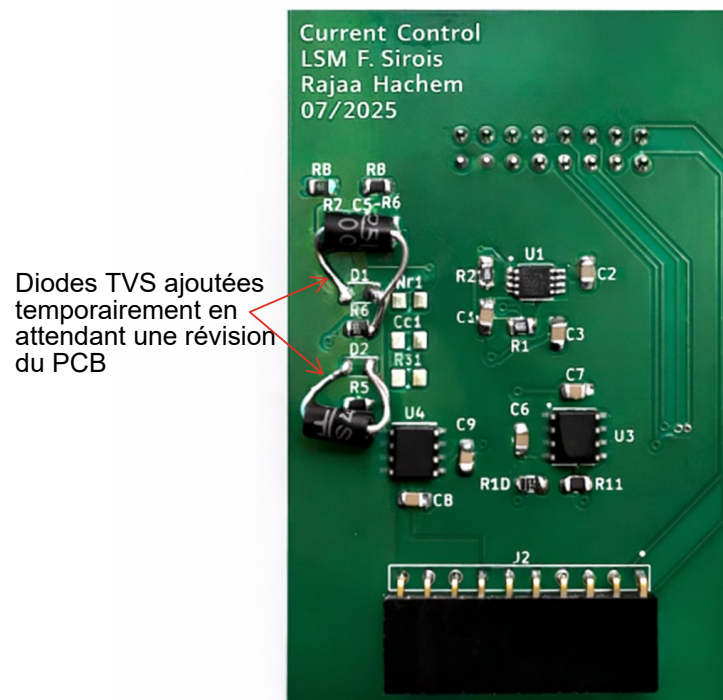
PCB de contrôle de courant – vue face 1.
